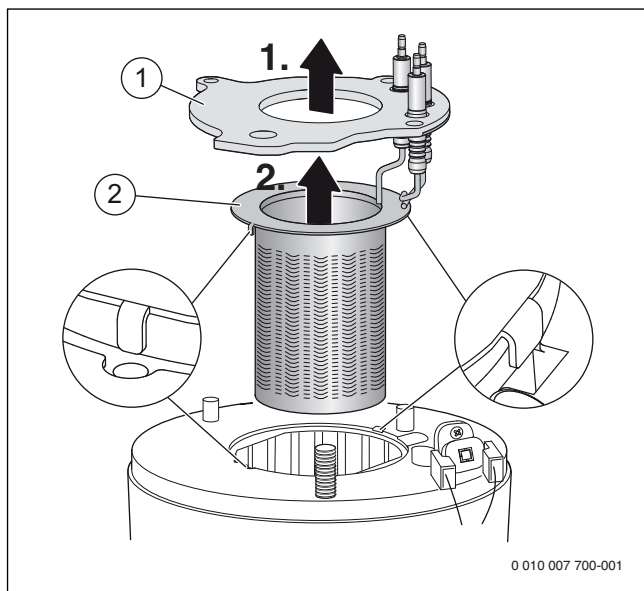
Remover o conjunto de eletrodos com vedação e queimador
